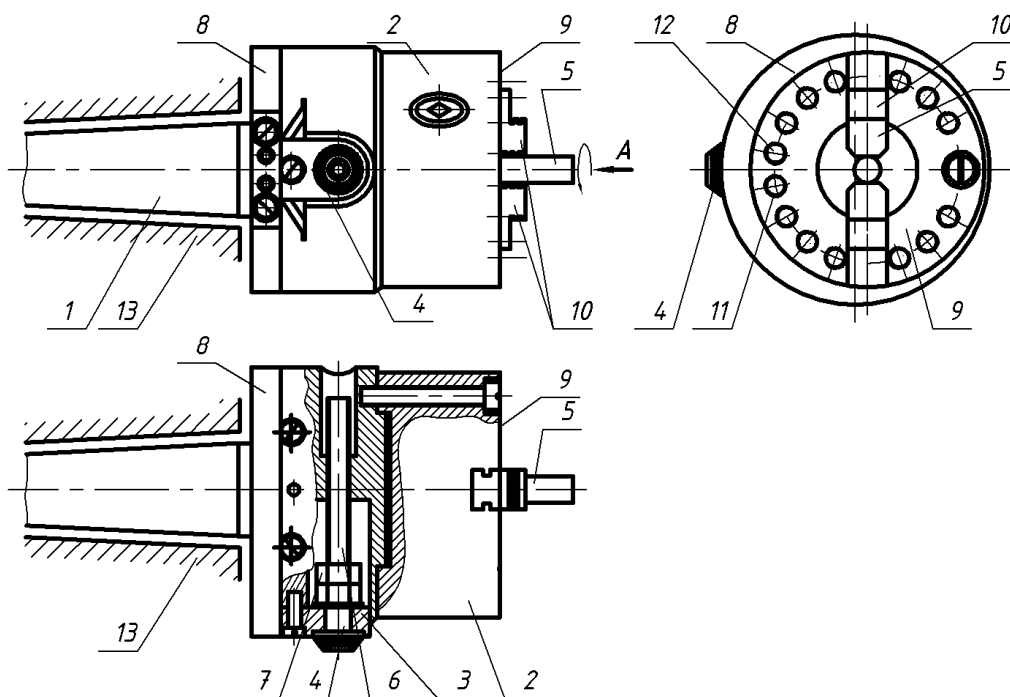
Токарний патрон для обробки ексцентричних поверхонь
